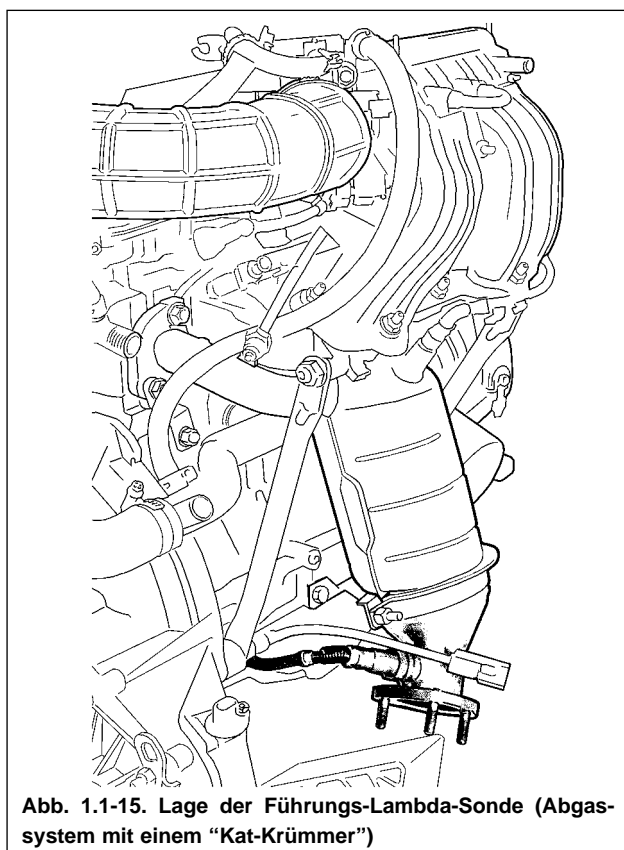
Lage der Führungs-Lambda-Sonde (Abgas-System mit einem "Kat-Krümmen")
